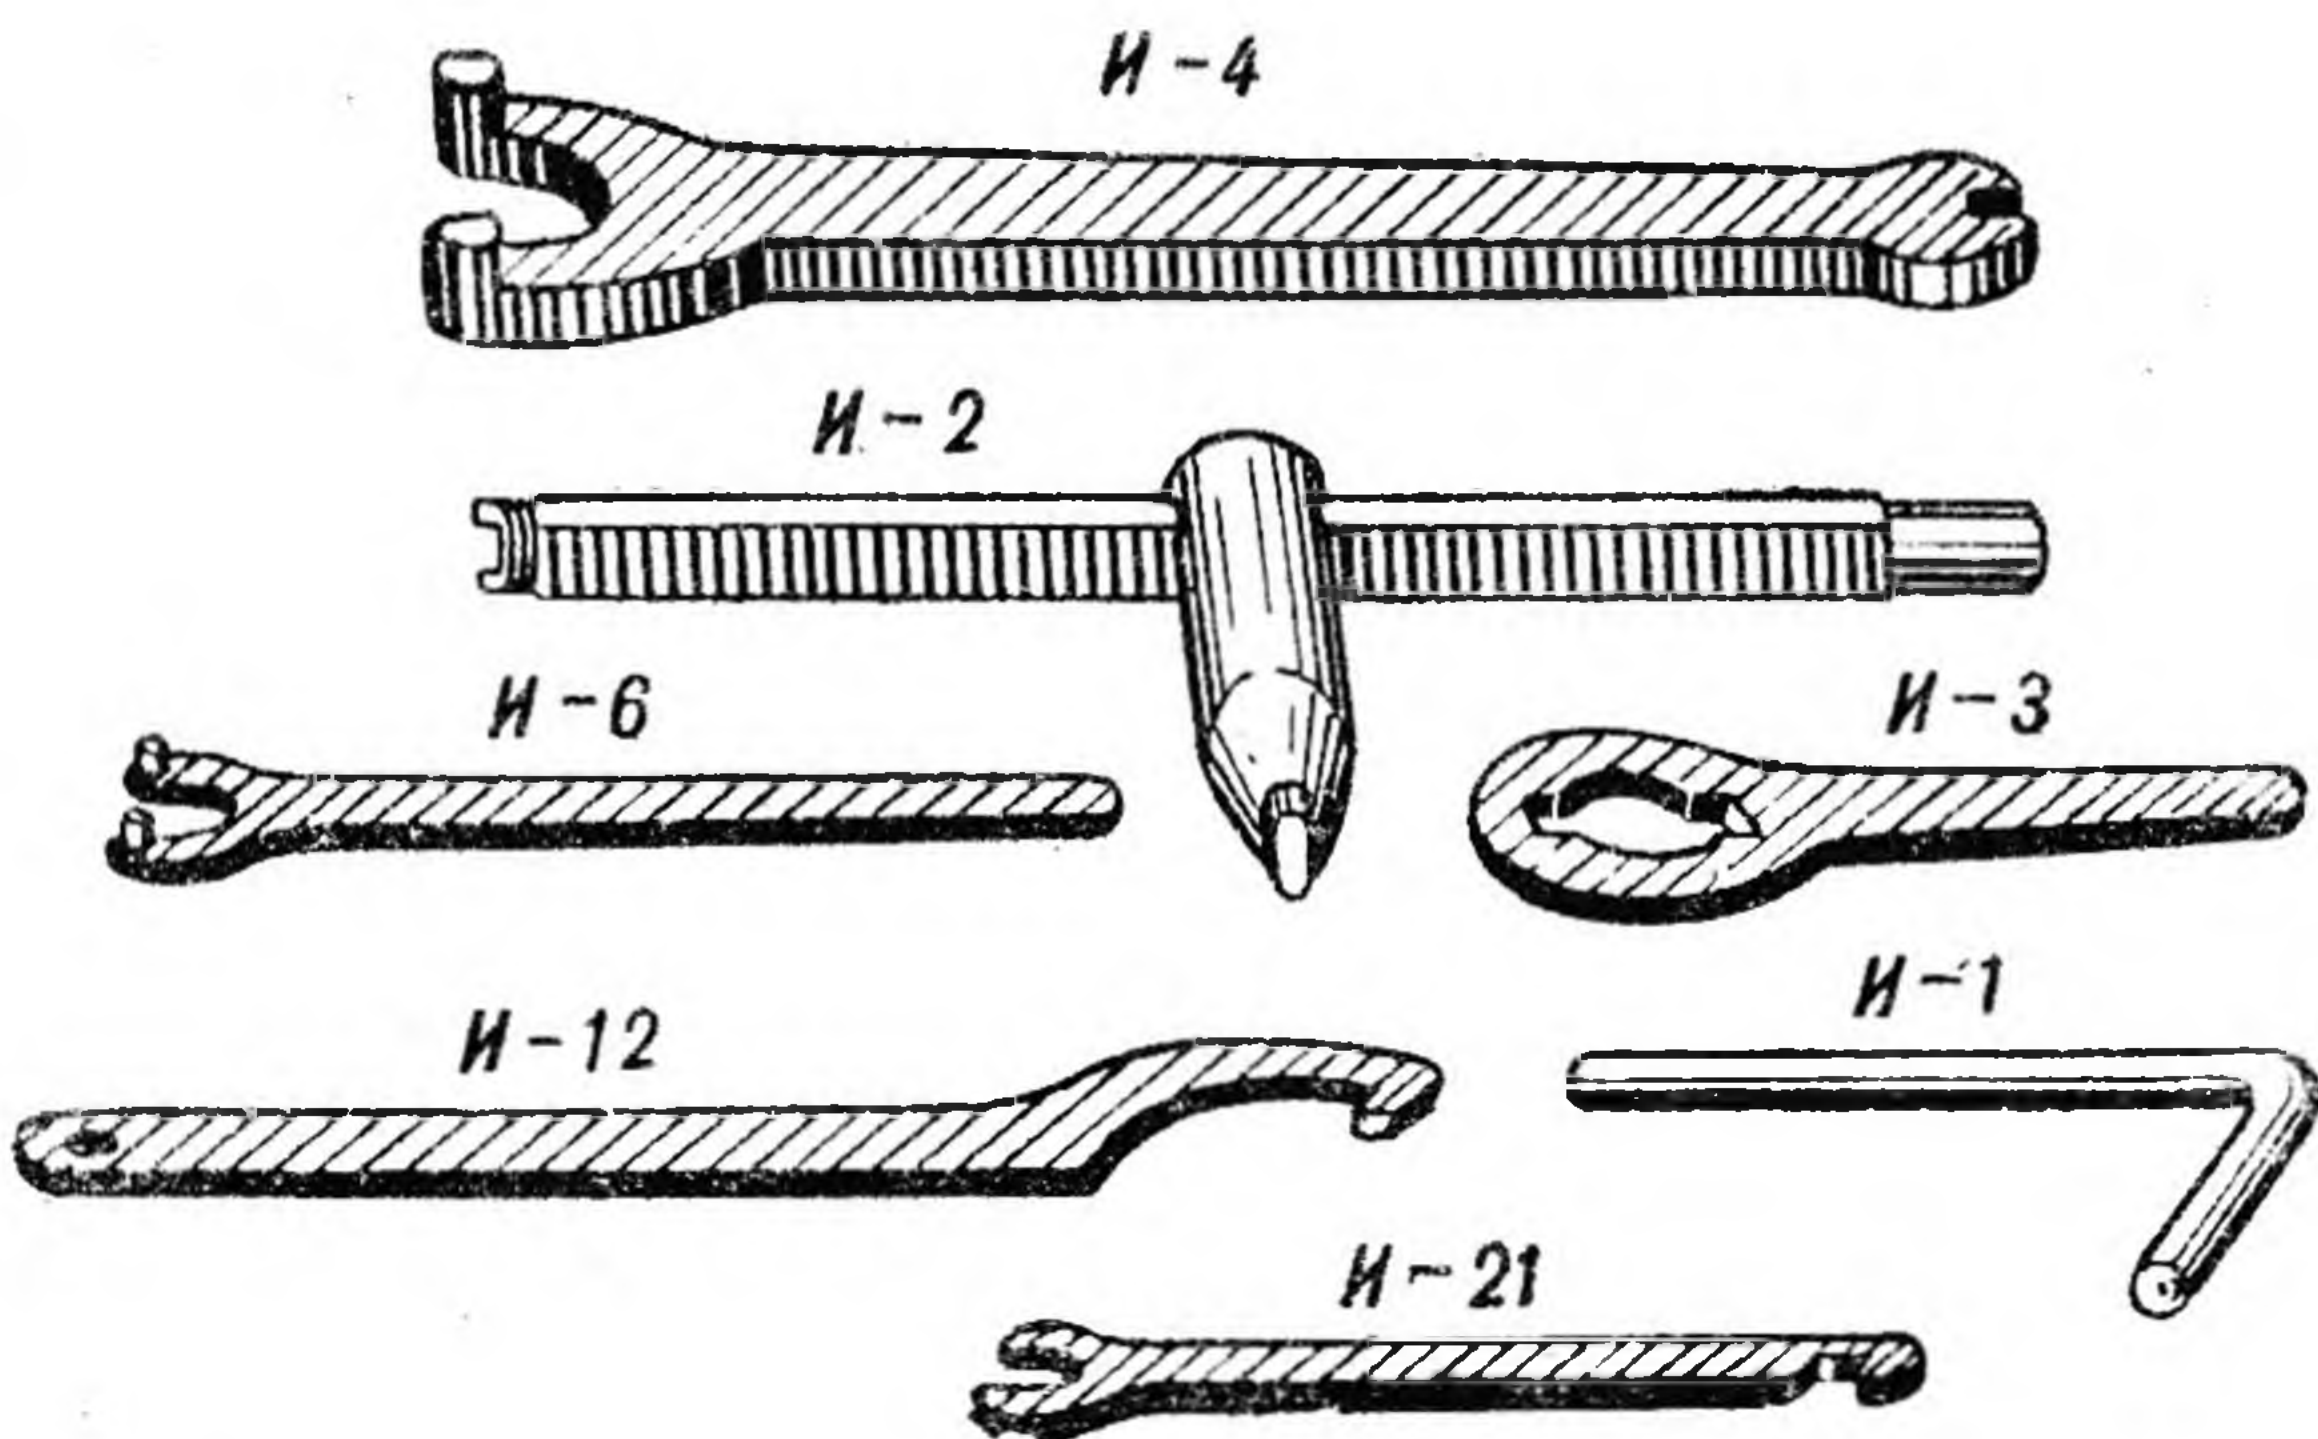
Инструмент для разборки и сборки затвора и полуавтоматики
